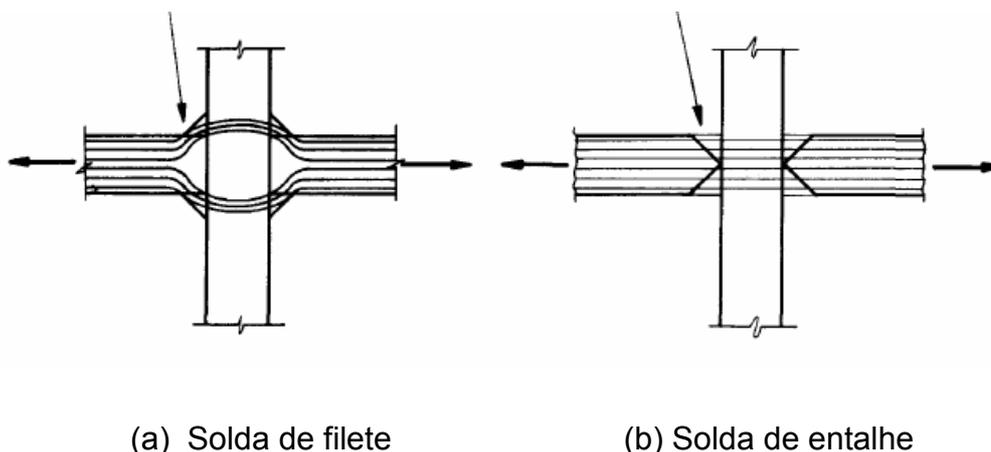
Fluxo de tensões em solda de filete e solda de entalhe – IBS/CBCA (2004)
